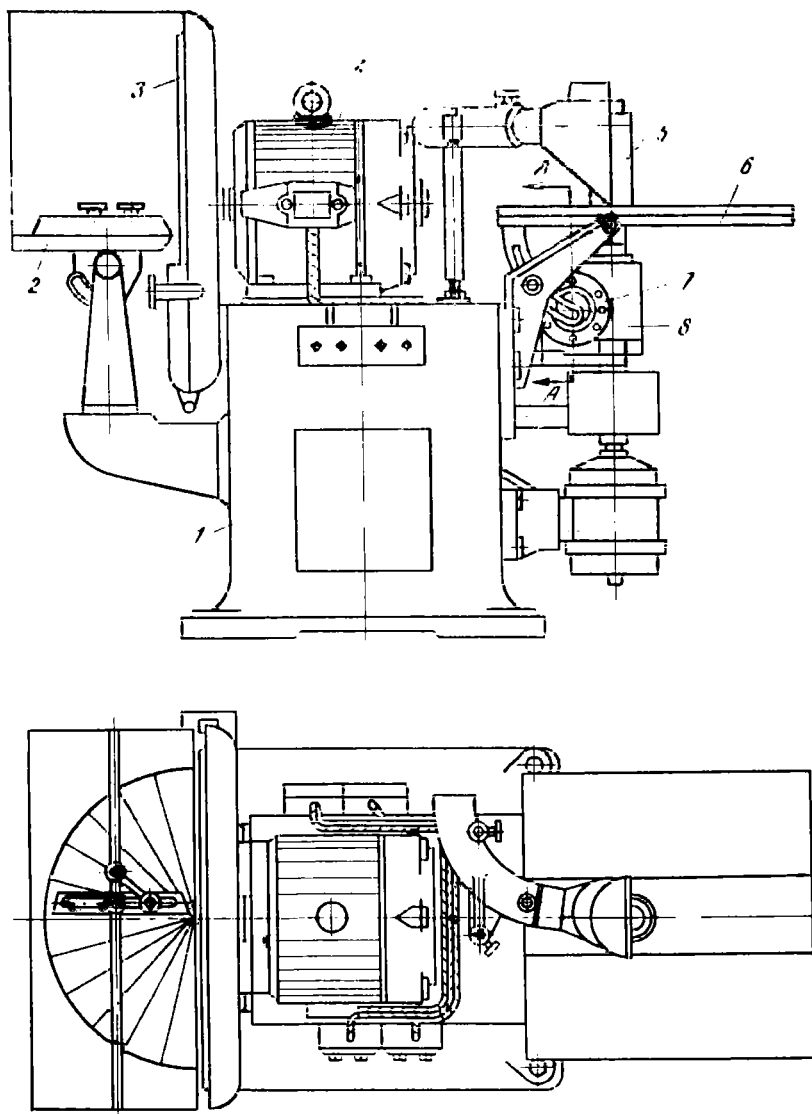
Схема шлифовального станка ШЛДБ-4:
